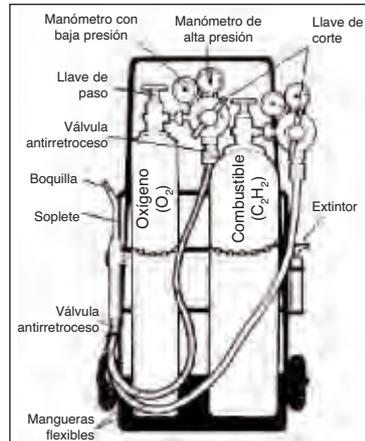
Equipo con botellas para soldadura oxiacetilénica
